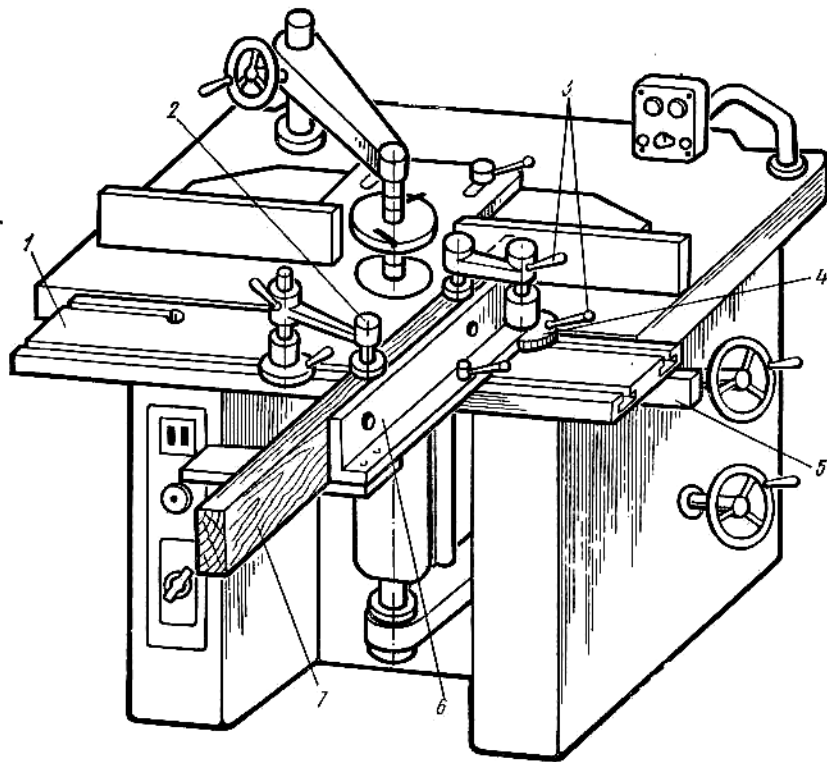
Фрезерный станок с шипорезной кареткой:
